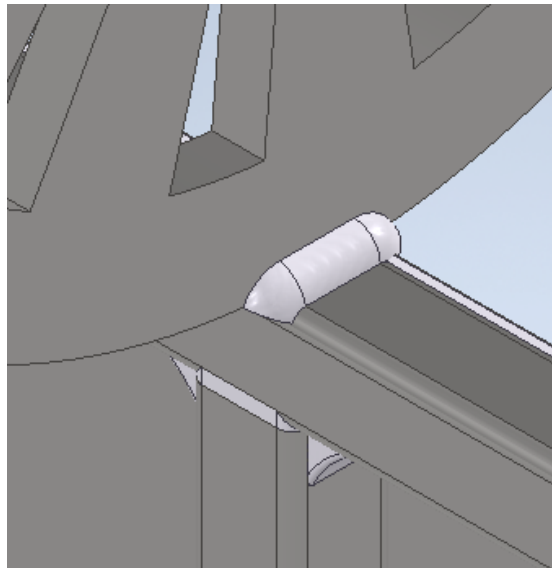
Refuerzo estructural del álabe después de la modificación.
